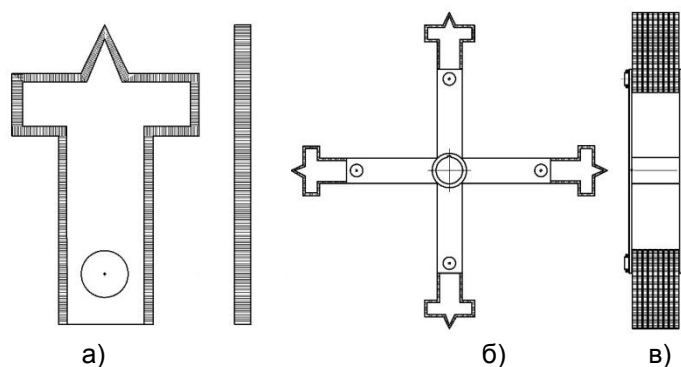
Молотки малогабаритної зернової кормодробарки;
